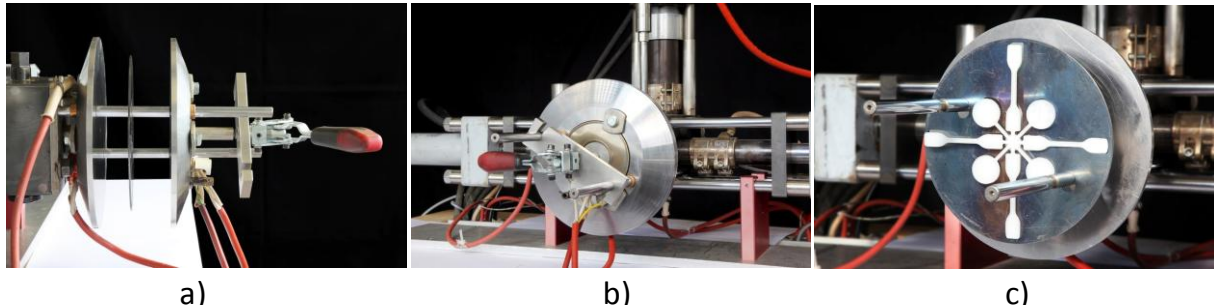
Description du moule thermorégulé. a) Mise en place des deux faces du moule et de l'insert, b) fermeture du moule et injection de la matière, c) récupération de la forme injectée.
